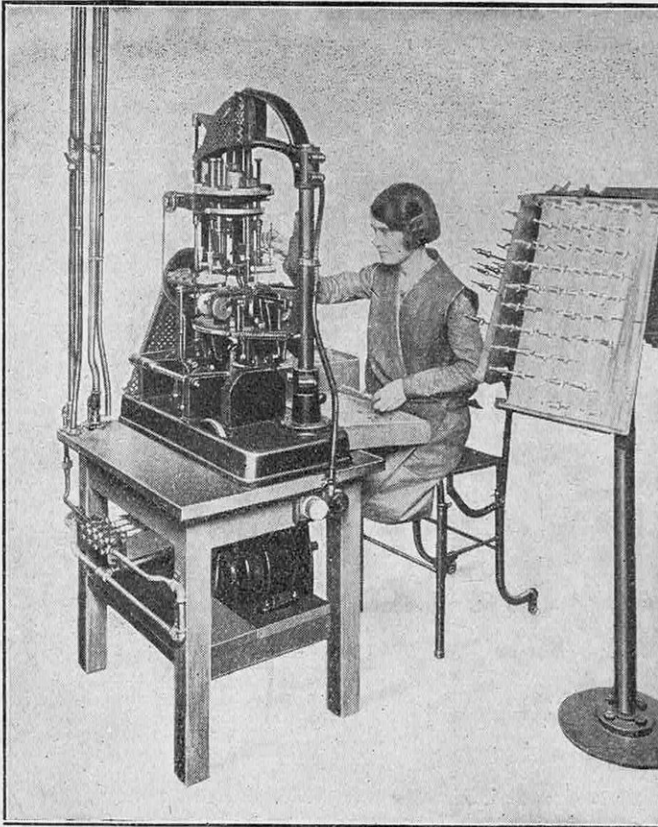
LA FABRICATION DES SUPPORTS DE FILAMENTS
